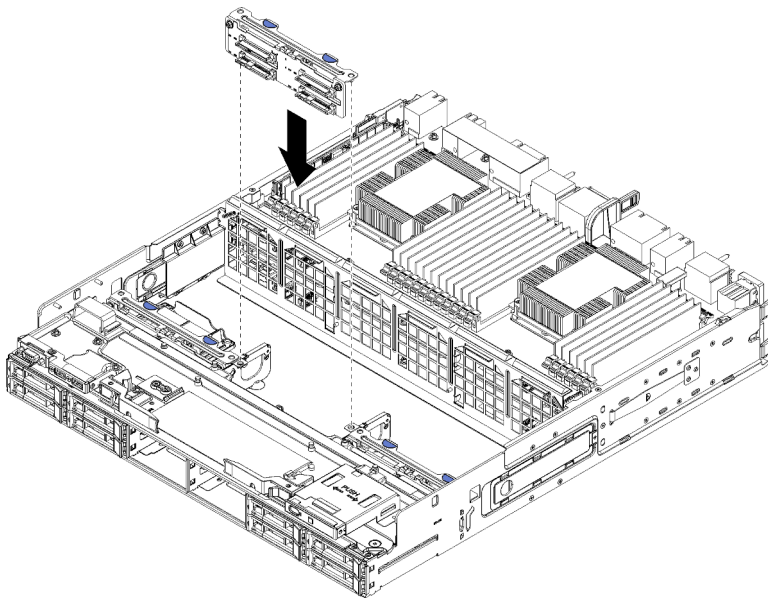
Installazione del backplane dell'unità disco fisso (inferiore)
